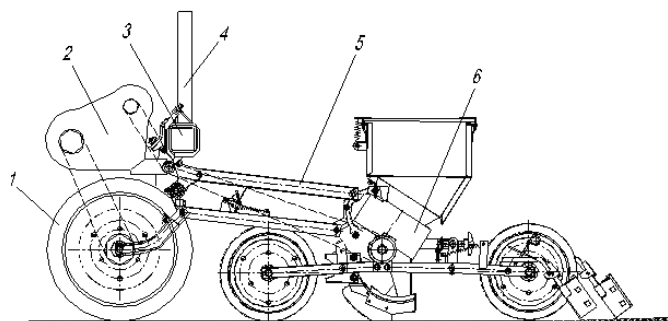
Конструктивна схема експериментальної сівалки для висіву широкорядним способом дрібного насіння сільськогосподарських культур малими нормами з вібраційно-дисківими висівними апаратами: 1 – опорно-приводні колеса; 2 – редуктор; 3 – рама; 4 – начіпка; 5 – паралелограмний механізм підвіски; 6 – експериментальні посівні секції з вібраційно-дисківими висівними апаратами.
